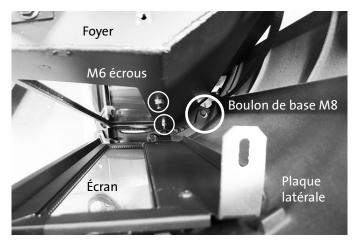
La vue est montrée en regardant entre la chambre de combustion et la plaque latérale.
